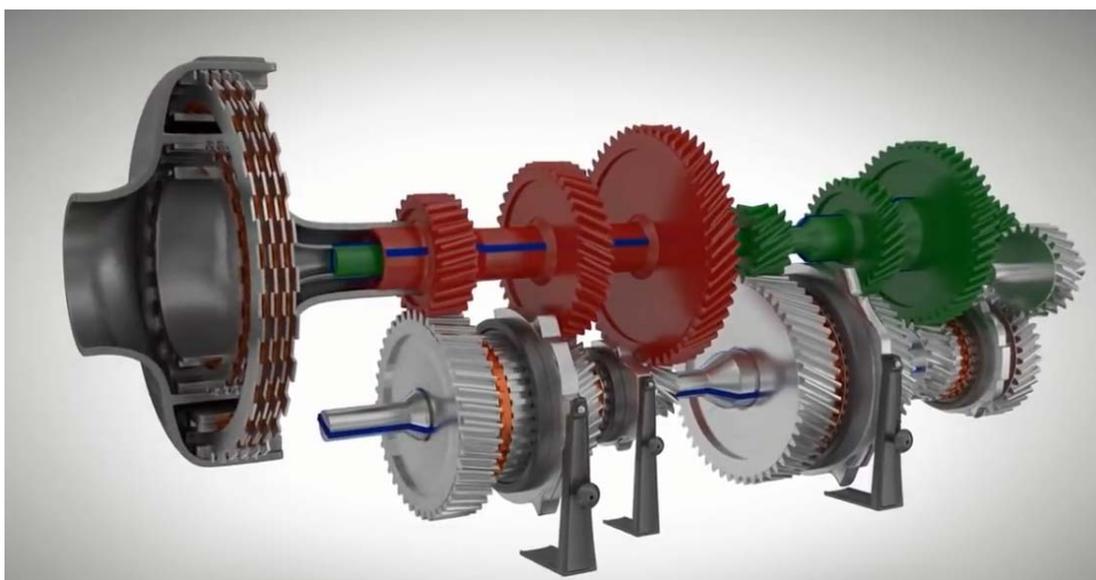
схема передачи крутящего момента роботизированной коробки передач.
